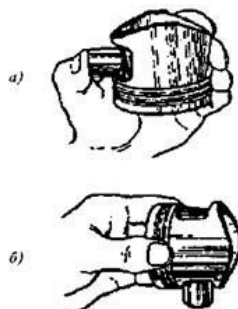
Установка поршневого пальца (а) и проверка его посадки (б)
